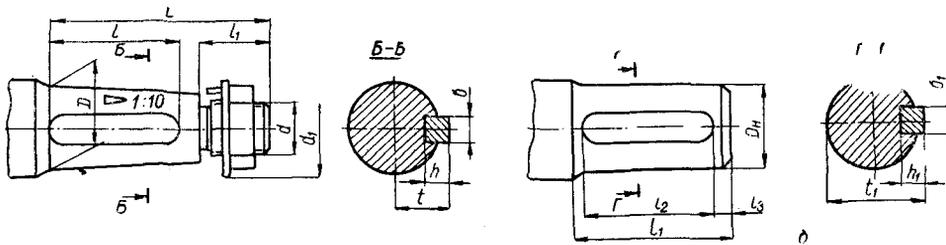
Присоединительные размеры концов валов мотор-редукторов МРА:
